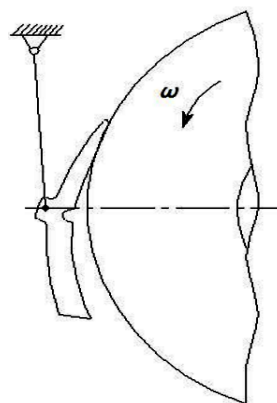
Загальний вигляд клиноподібного спрацювання колодки
